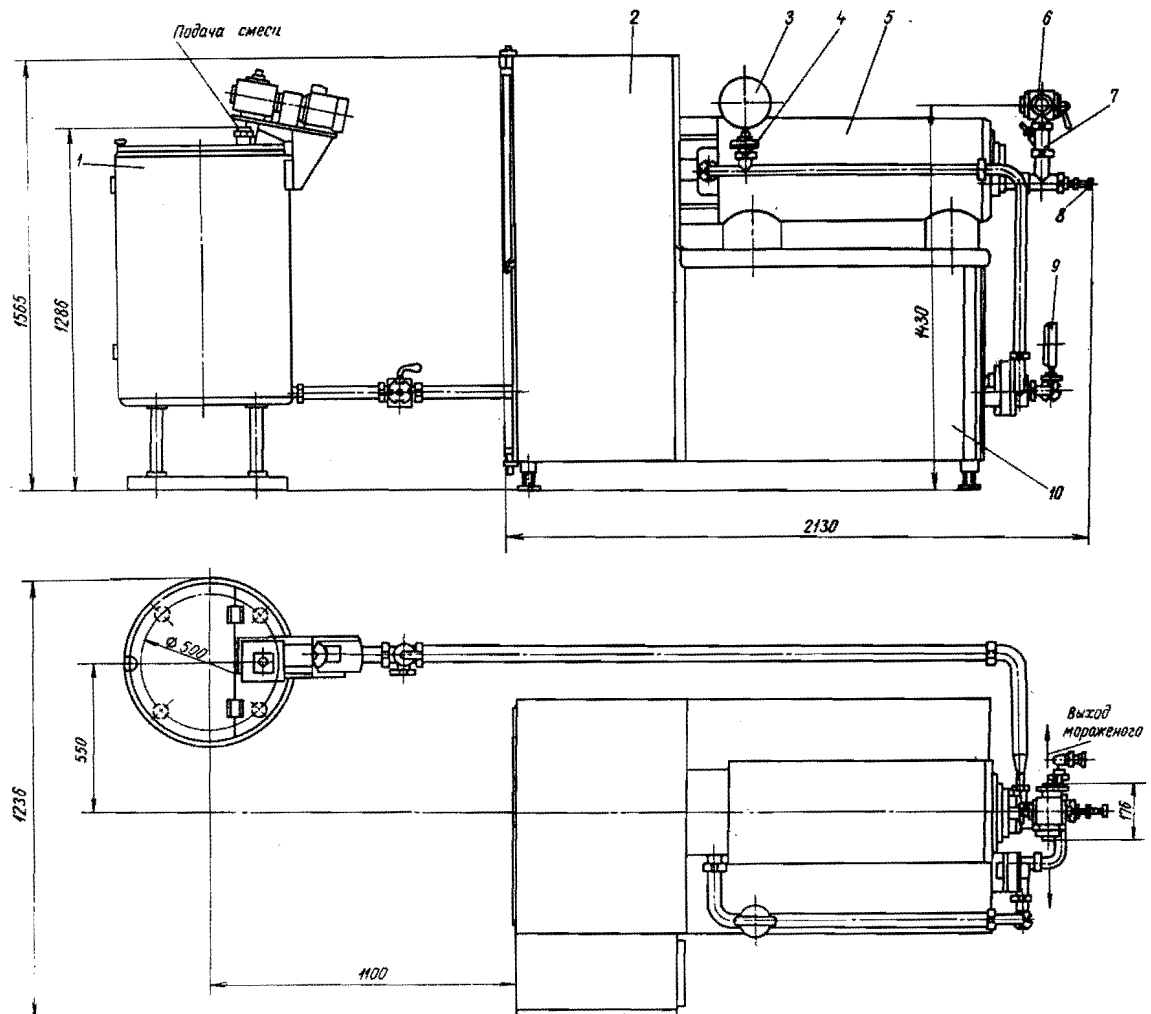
Общий вид фризера марки Б6-ОФШ для мороженого:
